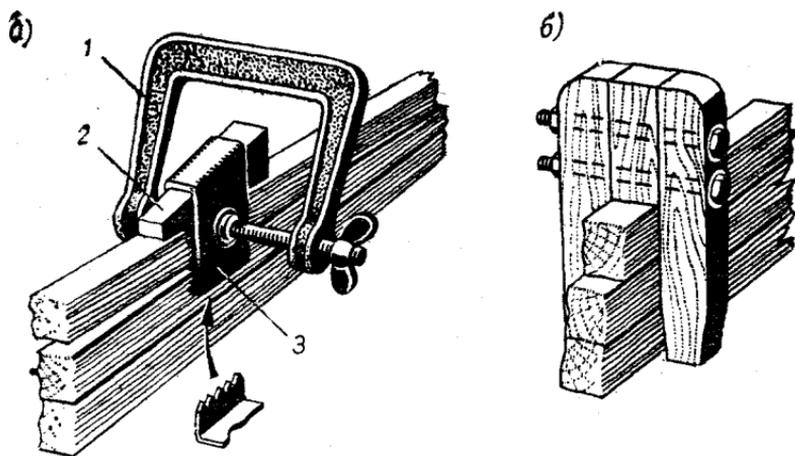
Приспособления для сборки реечной обшивки: *а* — клиновой прижим к струбцине; *б* — цвинка.
